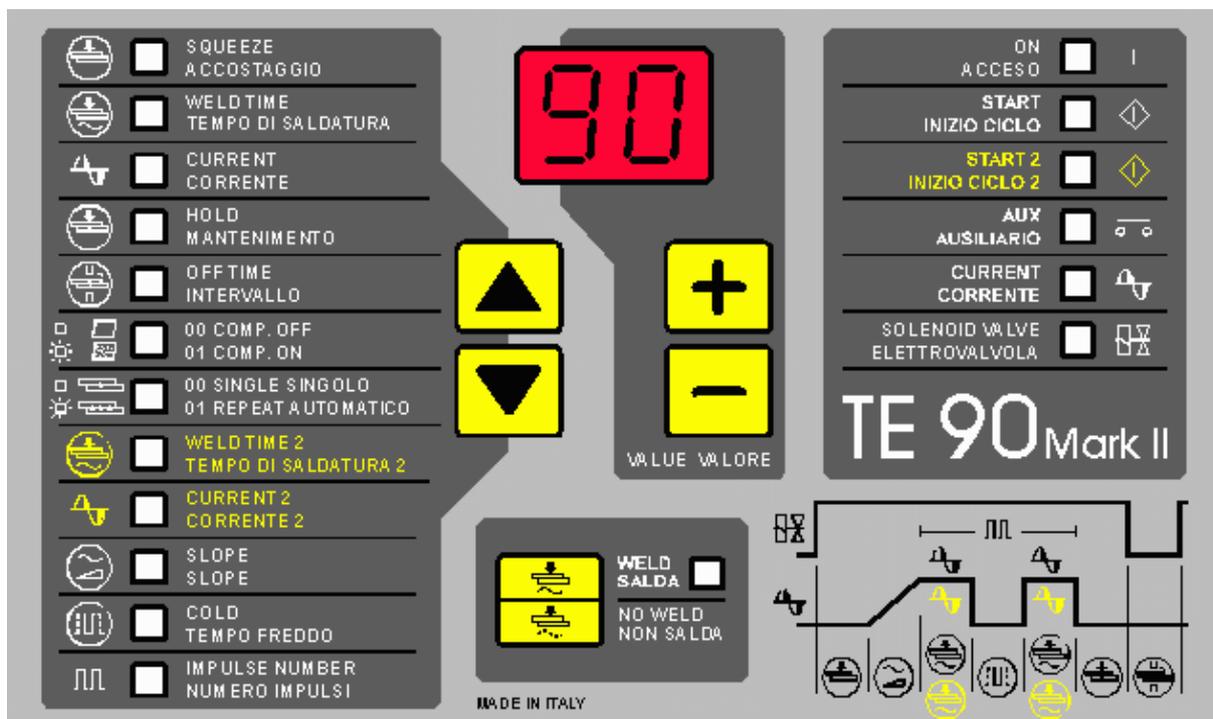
Dispositif de contrôle de soudage TE90 MARK 2
